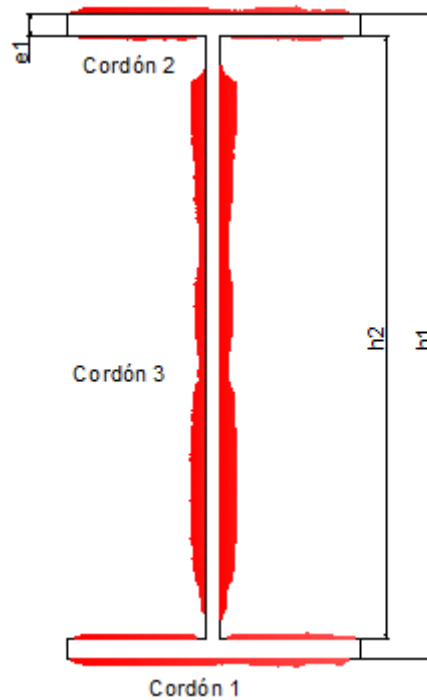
Cordones de soldadura expuestos en el perfil.
